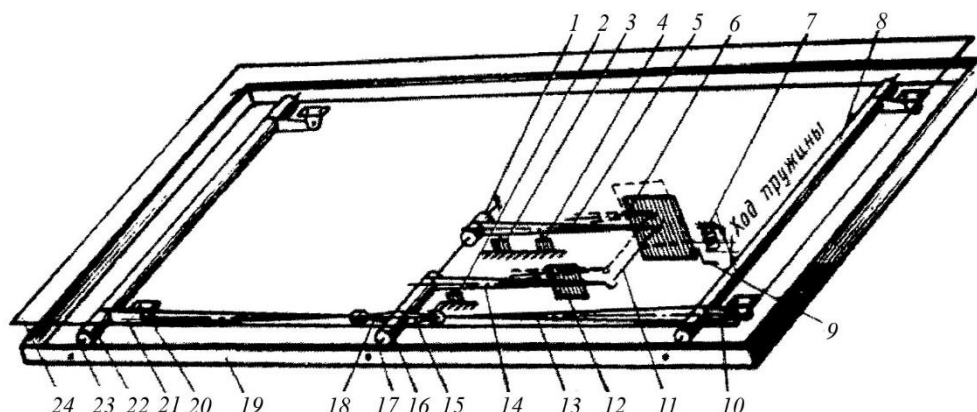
Схема грузового механизма контроля загрузки с подвижным полом:
